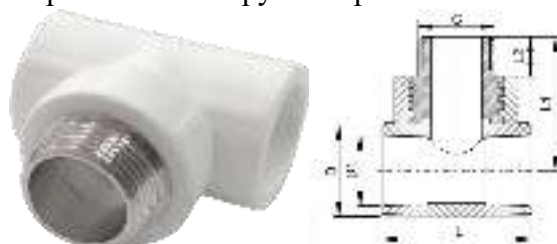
Тройник, комбинированный с внутренней резьбой
